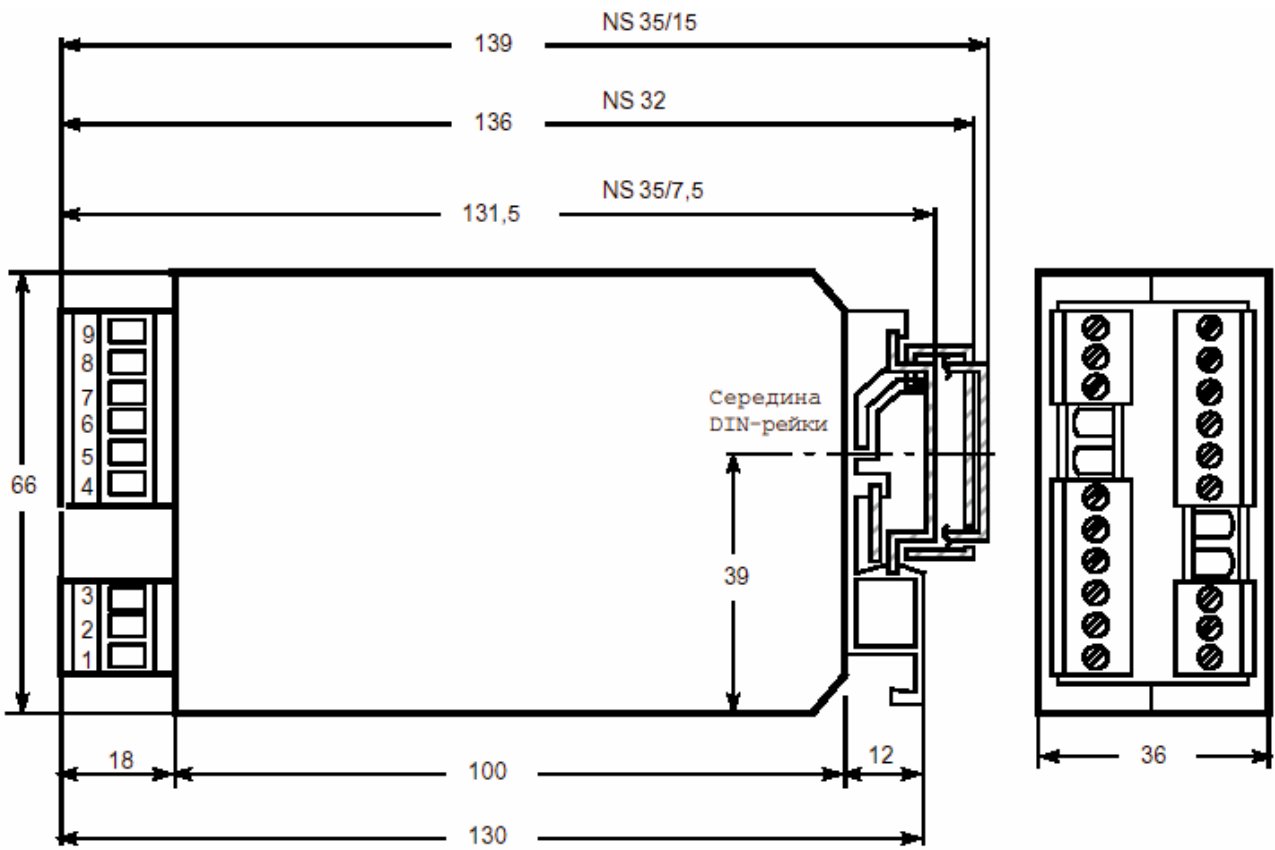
Габаритный чертеж соединительного реле, размеры в мм
